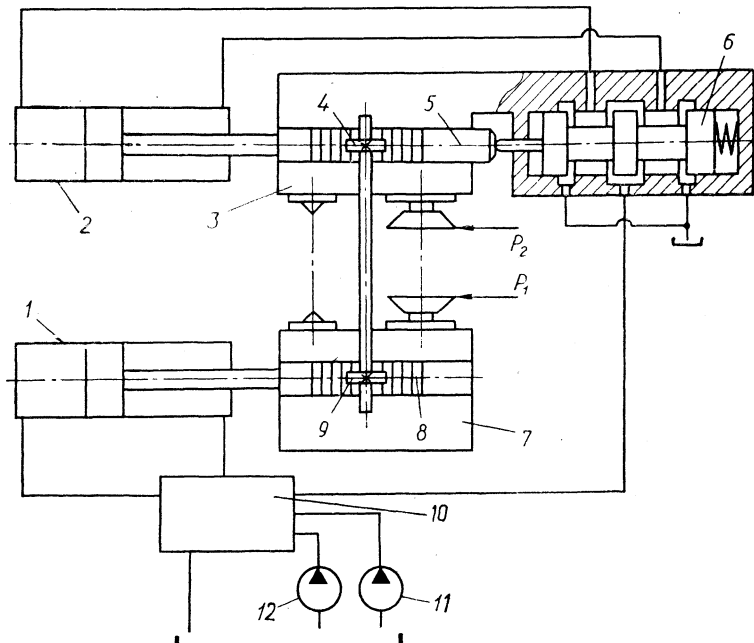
Схема синфазного привода робочих головок фрезерно-центрувальних напівавтоматів
